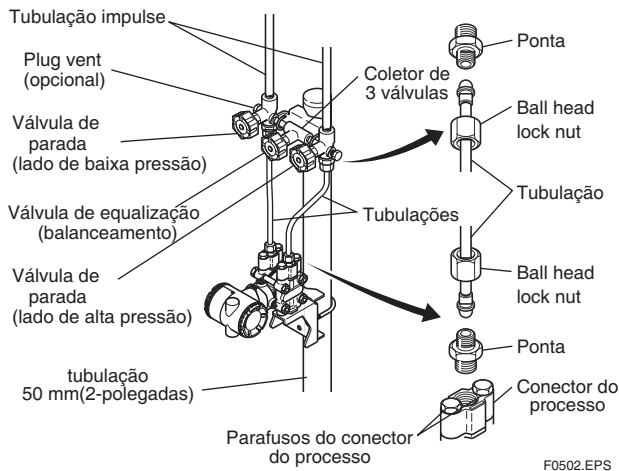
Coletor de 3 Válvulas (Tipo de Montagem de Tubulação)
